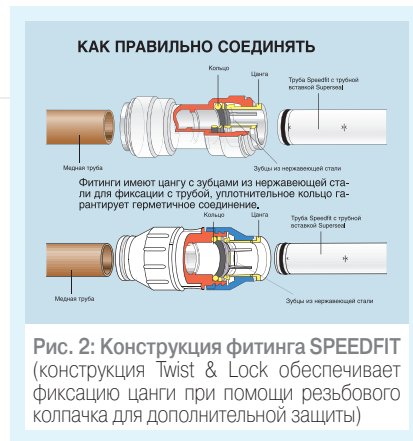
Конструкция фитинга SPEEDFIT (конструкция Twist & Lock обеспечивает фиксацию цанги при помощи резьбового колпачка для дополнительной защиты)
